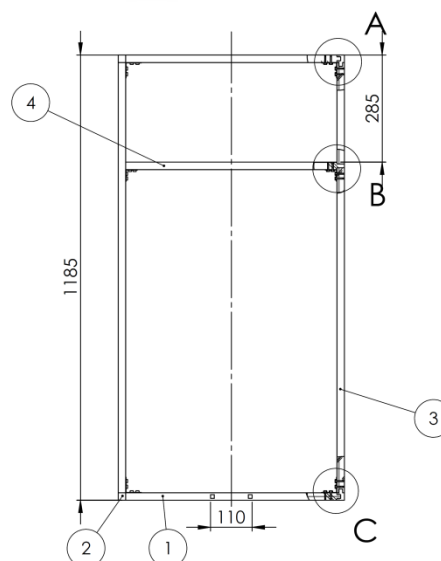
2: Vista frontal del ensamblaje de la estructura. Fuente: Elaboración propia.
